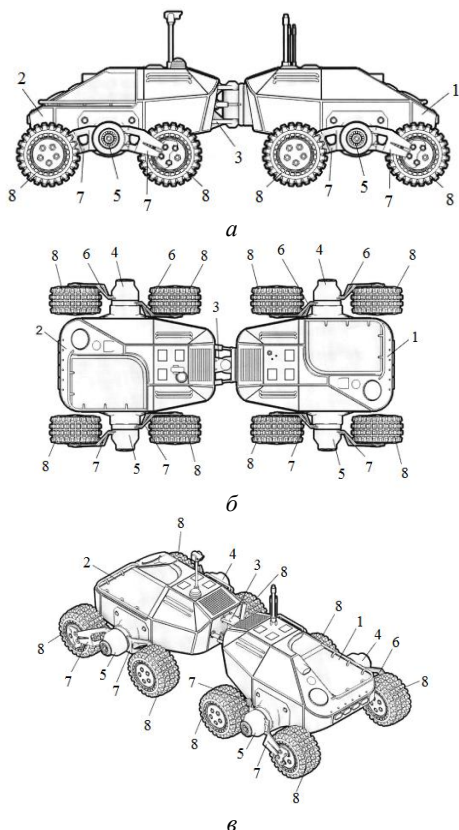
Зчленований транспортний засіб: *а* – вид збоку; *б* – вид зверху; *в* – вид в ізометрії: 1 – передня корпусна секція; 2 – задня корпусна секція; 3 – зчпний пристрій; 4 – ліві механізми повороту поздовжніх важелів; 5 – праві механізми повороту поздовжніх важелів; 6 – ліві поздовжні важелі; 7 – праві поздовжні важелі; 8 – колеса
